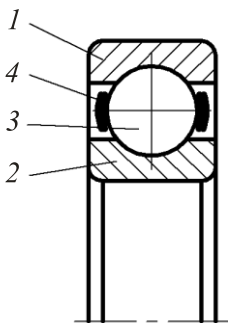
Шариковый однорядный радиальный подшипник качения
